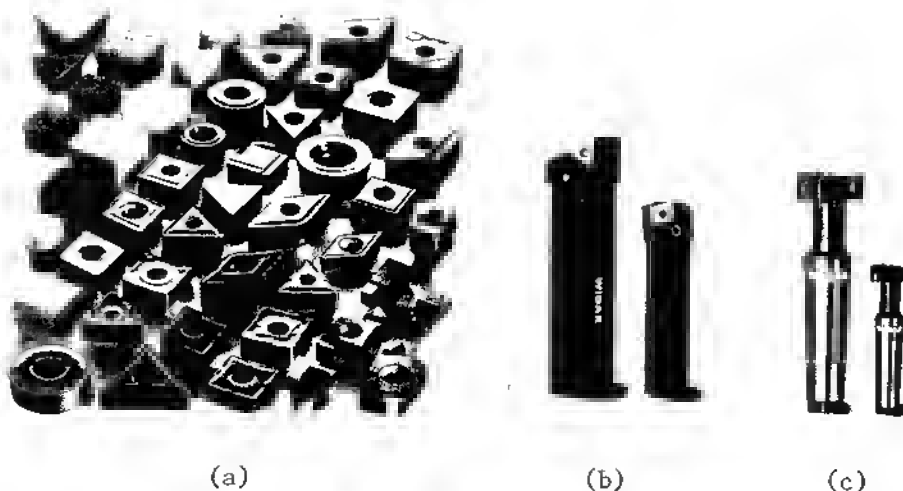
(a) Différentes formes de plaquettes d'usinage installées sur un porte-outil de tournage (b) et de fraisage (c).
